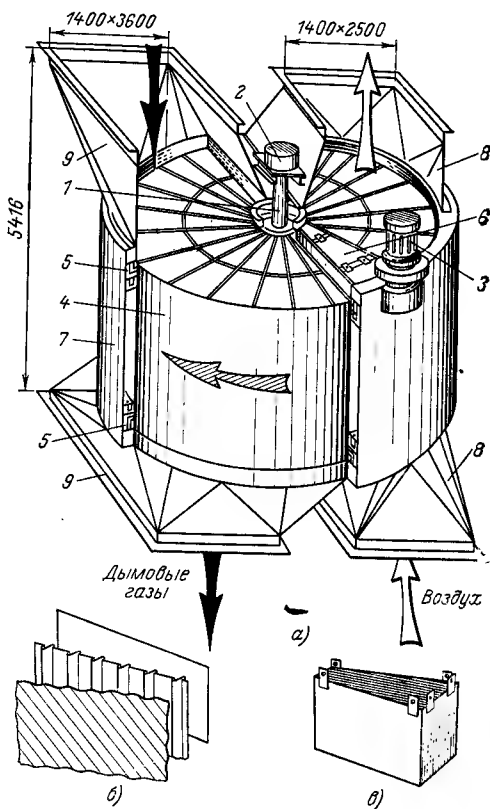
Регенеративный вращающийся воздухоподогреватель.
